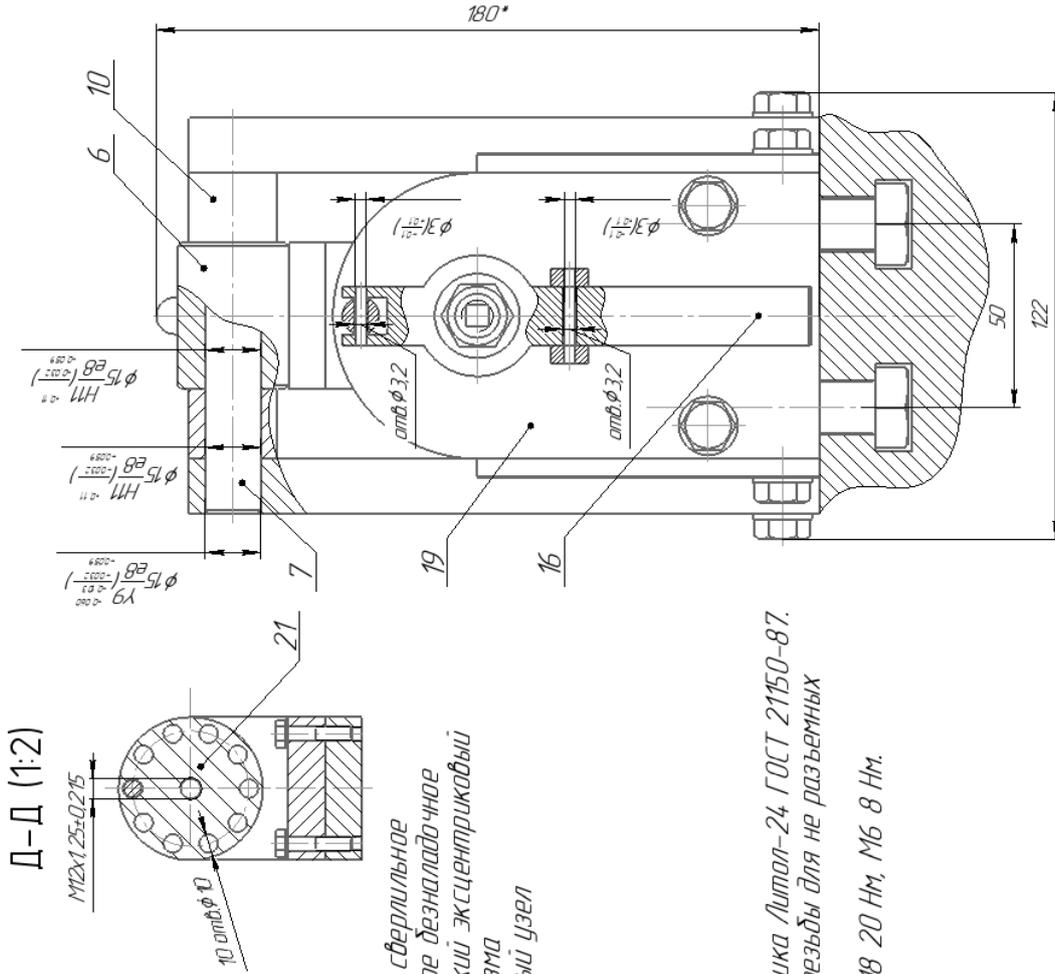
Сборочный чертеж приспособления (часть 2)
